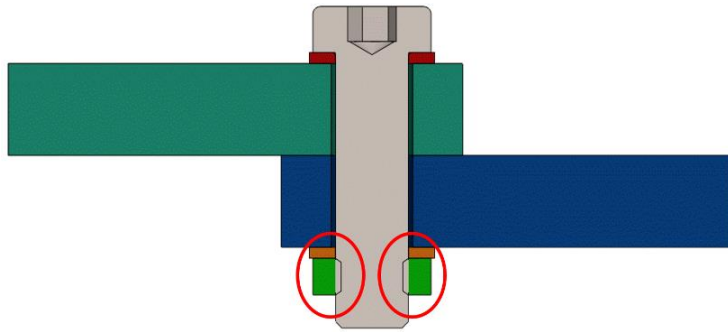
Schnittansicht einer Überschneidung der Gewindeflächen einer Schraube und Mutter im CAD-Modell
